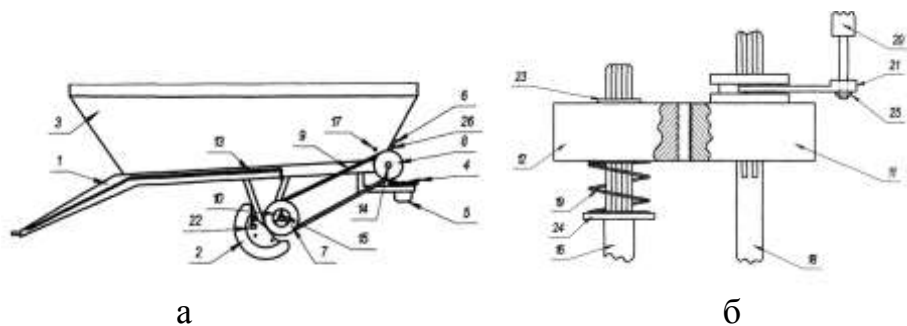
Схема конструкції агрегату для внесення мінеральних добрив: а - конструкція; б - механізм дозувального пристрою
